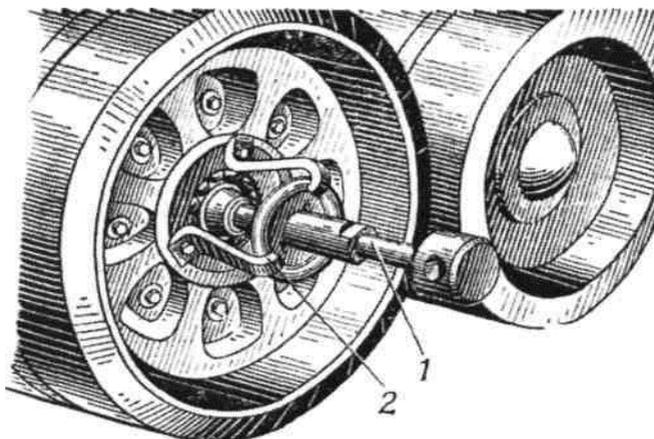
Установка приспособления УК–1СББ для спрессовки опорного катка с использованием винтового пресса:
